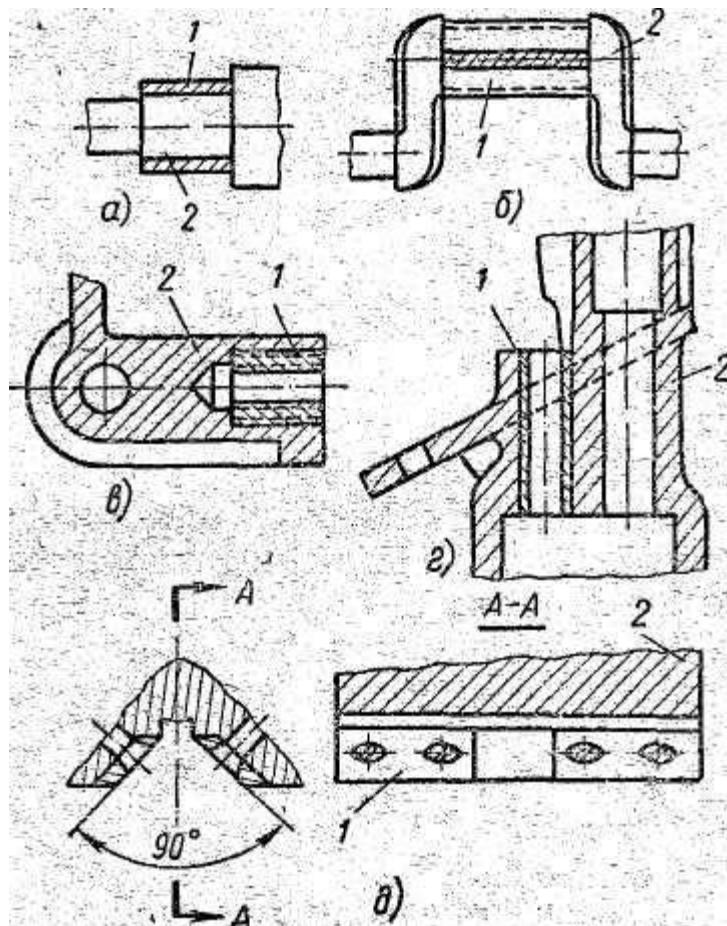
Типовые случаи применения дополнительных деталей при ремонте: а- установка на валу втулки, б- установка полувтулки на шейке коленчатого вала, в-установка втулки с резьбой, е-установка втулки в отверстие, и-установка планки на изношившейся плоскости; 1-деталь-компенсатор, 2-ремонтируемая деталь
